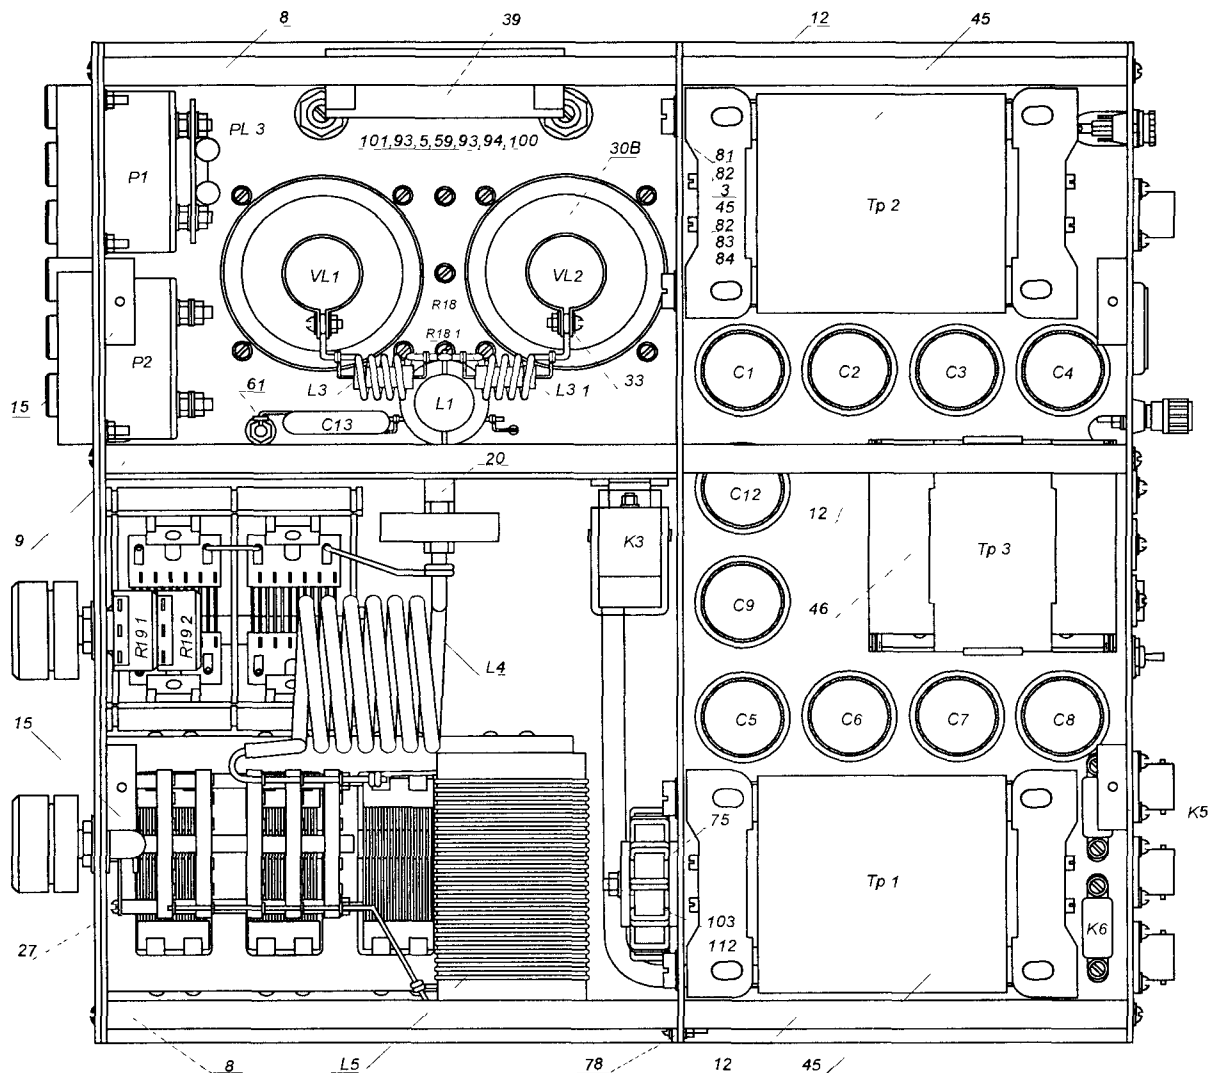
ВМ. Сборочный чертеж усилителя DVA-300BM. Вид сверху со снятой верхней крышкой (С возможностью режима "ОБХОД" и режимом "3-2")
